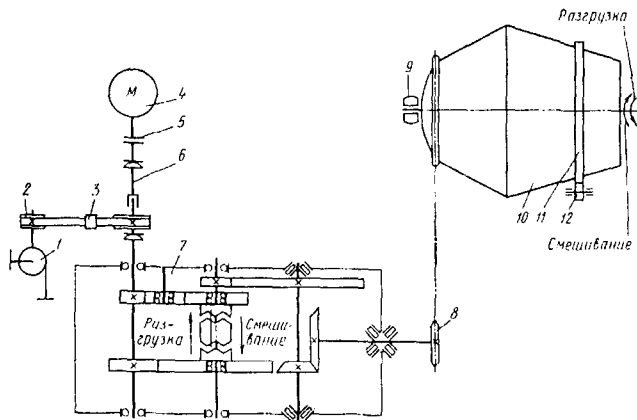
Кинематическая схема автобетоносмесителя: 1 – насос для подачи воды; 2 – ведущий шкив; 3 – натяжной ролик; 4 – двигатель; 5 – муфта сцепления; 6 – карданный вал; 7 – редуктор; 8 – цепная передача; 9 – главный опорный подшипник; 10 – барабан; 11 – бандаж; 12 – опорный ролик.
